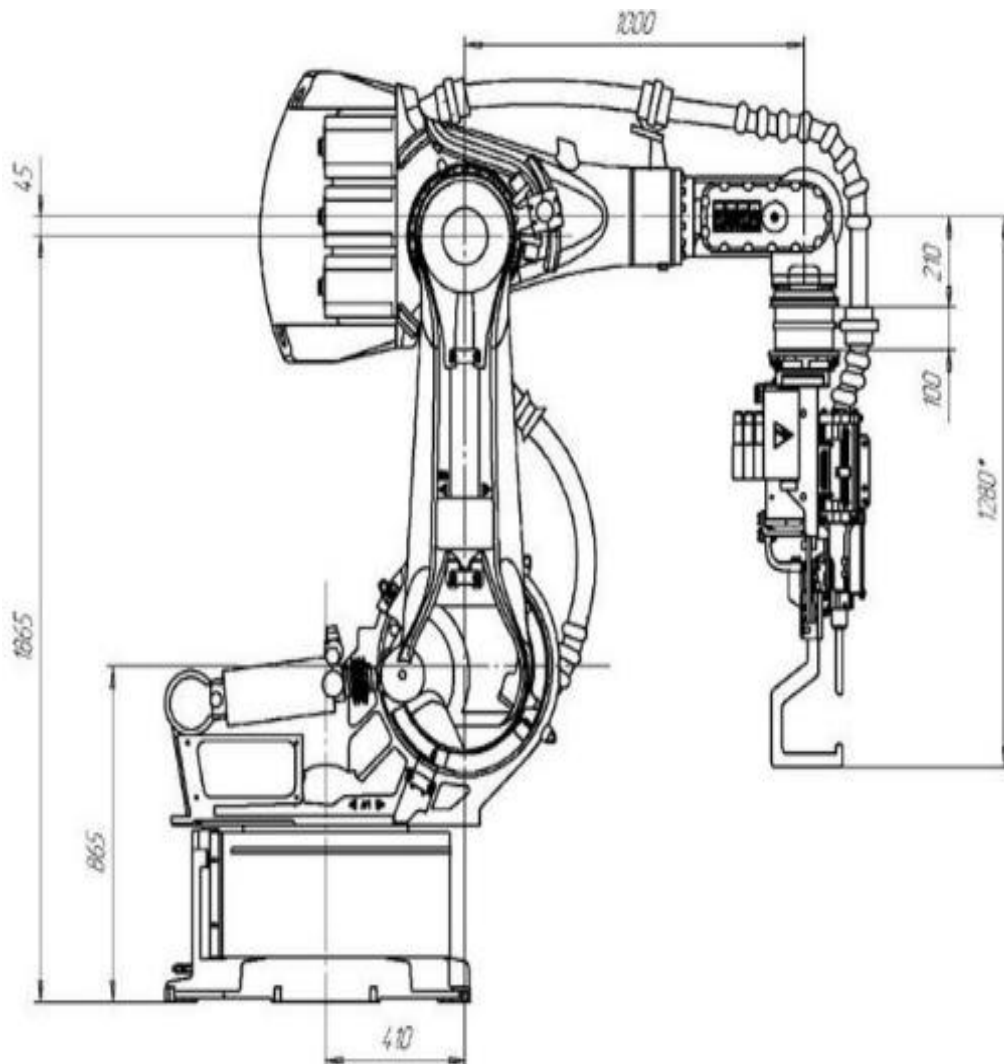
Конструкція робота для дугового зварювання FANUC ARC Mate 100iC/12
